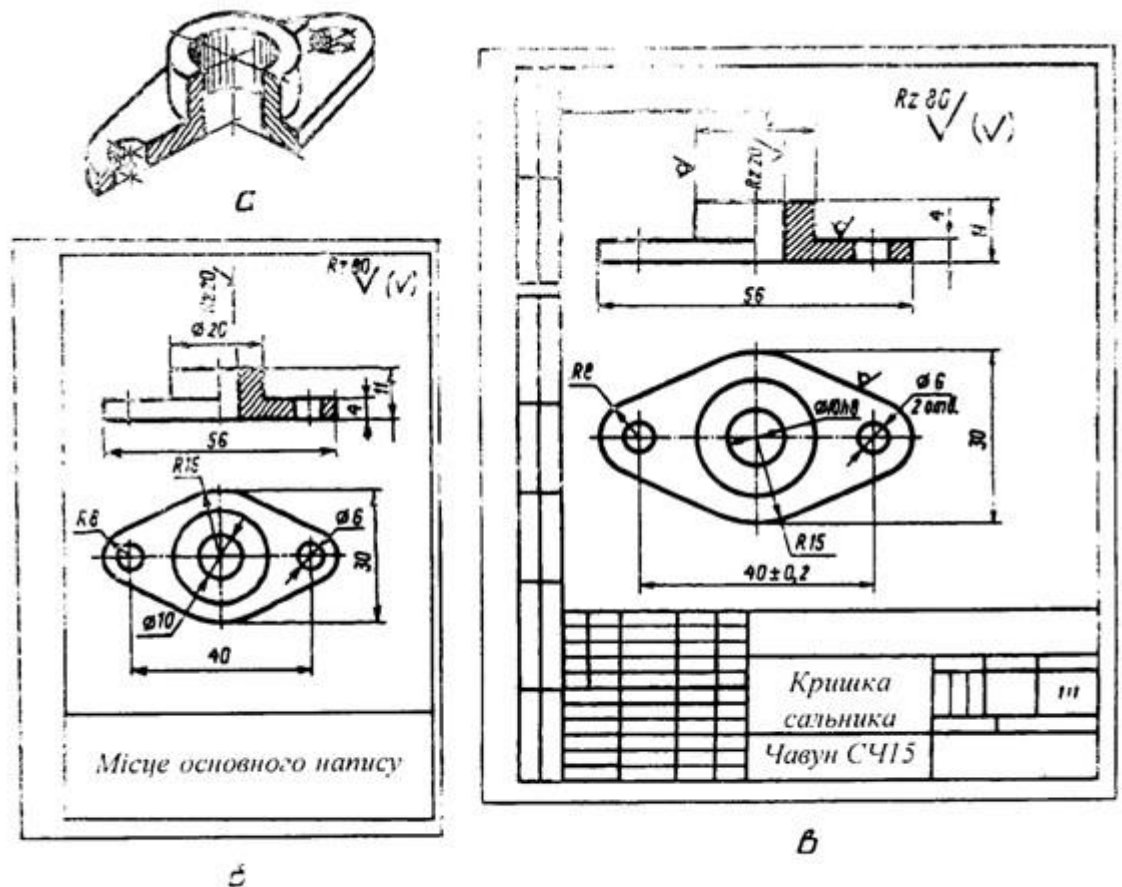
Ескіз (б) і креслення (а) деталі (а).
